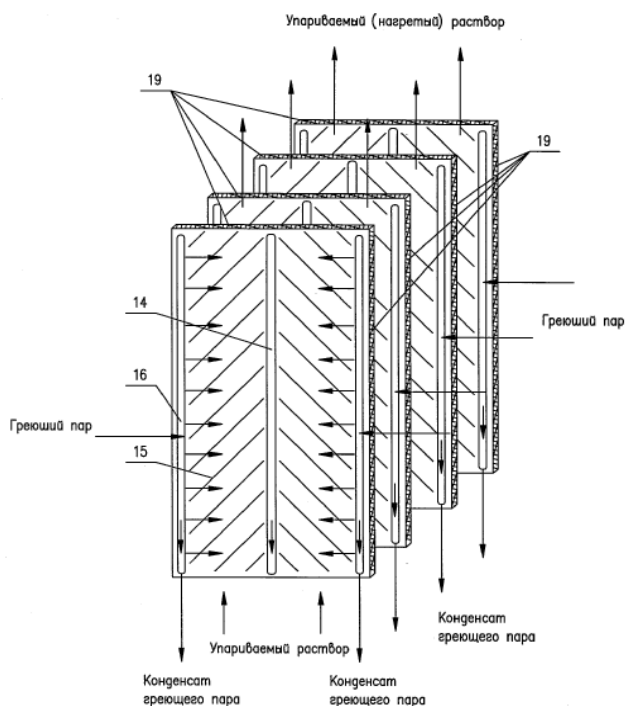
Компоновка попарно сваренных пластин разборной греющей камеры
